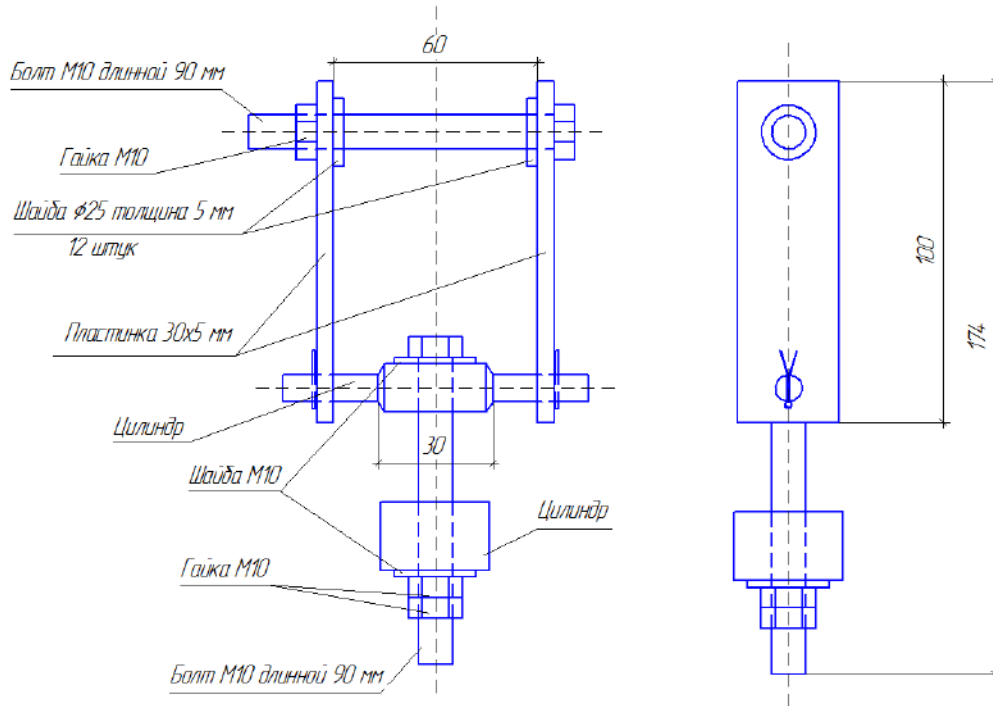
Конструкция стальных крепежных приспособлений (элементы 6, 7 на рис. 4.14)
